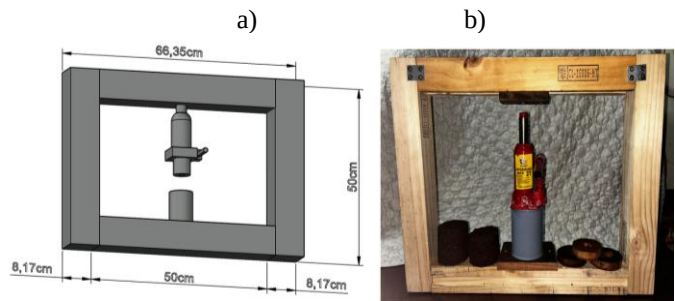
a) Diseño y medidas de la máquina para la fabricación de briquetas y b) Briquetadora final construida.
